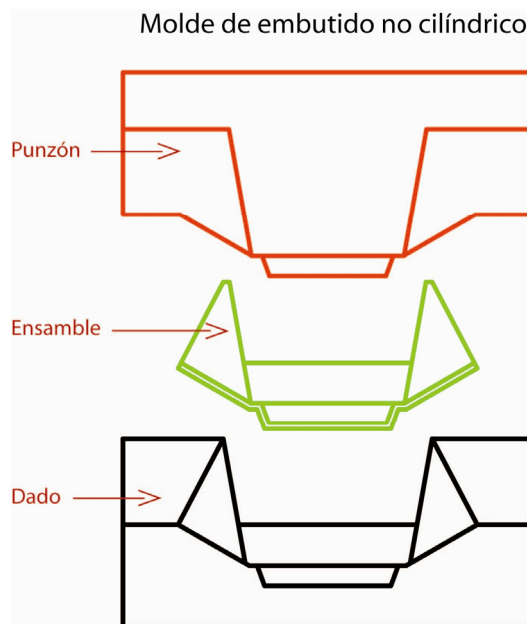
Croquis del molde de embutido no cilíndrico.
